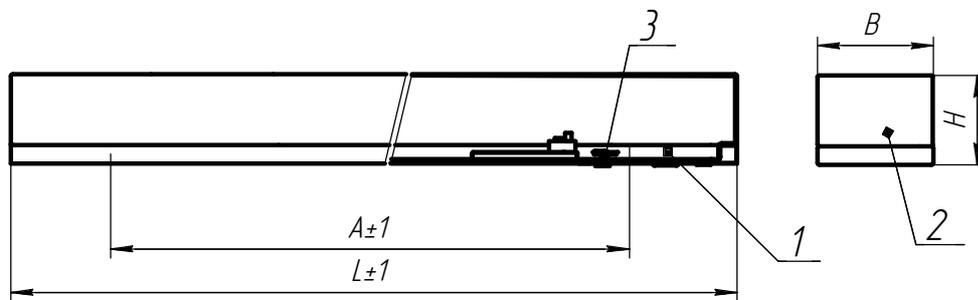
ДПО46-19; 38; 76 1. корпус в сборе; 2. рассеиватель; 3. зажим
